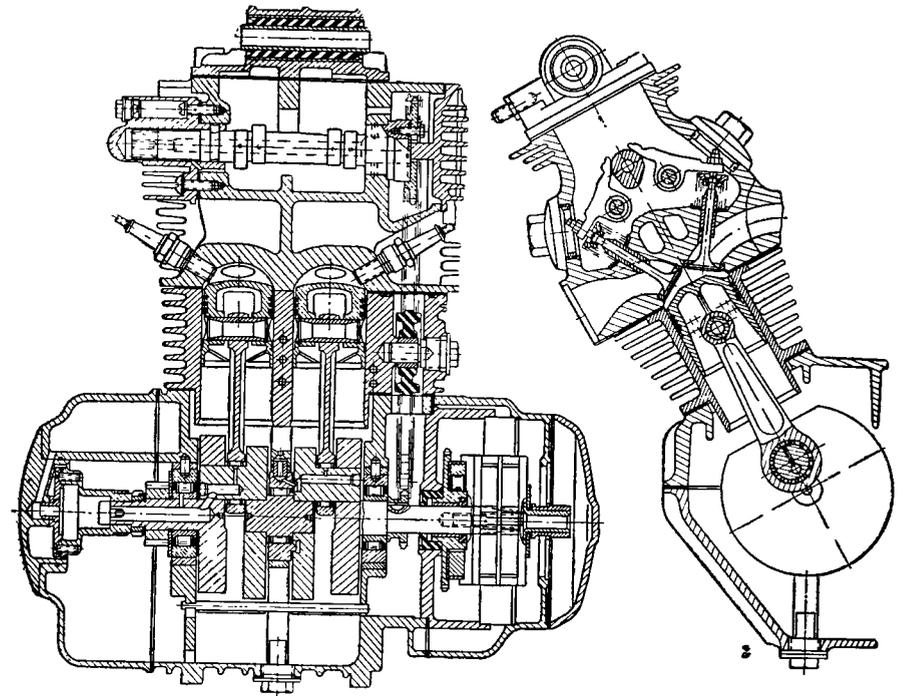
Схема спортивно-дорожного двигателя Honda CB-92 с одним верхним распределительным валом.
